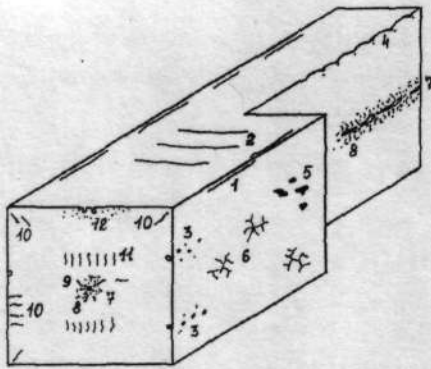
Схематическое представление основных видов дефектов, встречающихся в непрерывнолитой сортовой заготовке: 1 – продольные угловые трещины; 2 – поперечные трещины; 3 – поры; 4 – следы качания кристаллизатора; 5 – загрязнения на поверхности заготовки; 6 – паукообразные трещины; 7 – осевая пористость; 8 – осевая химическая неоднородность; 9 – осевые трещины; 10 – трещины угловые и перпендикулярные граням; 11 – деформационные трещины; 12 – точечная неоднородность
